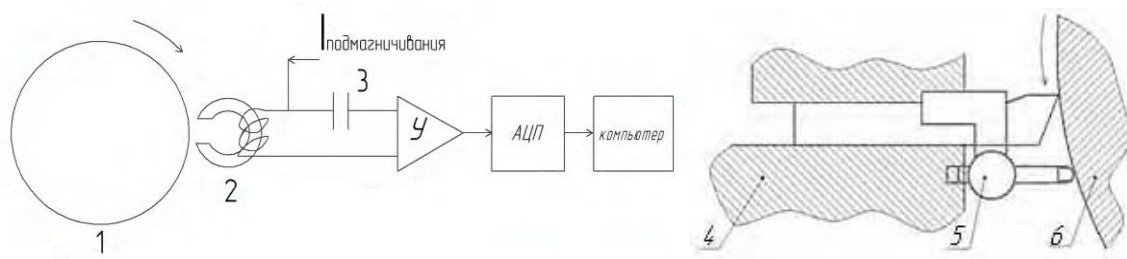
Схема установки магнитной головки на резцедержатель для получения и анализа полезного сигнала: 1 – контролируемая вращающаяся деталь, 2 – магнитная головка, 3 – разделительный конденсатор, 4 – резцедержатель; 5 – магнитная головка на микрометрическом винте; 6 – контролируемая деталь, У – усилитель, АЦП – аналогово-цифровой преобразователь
